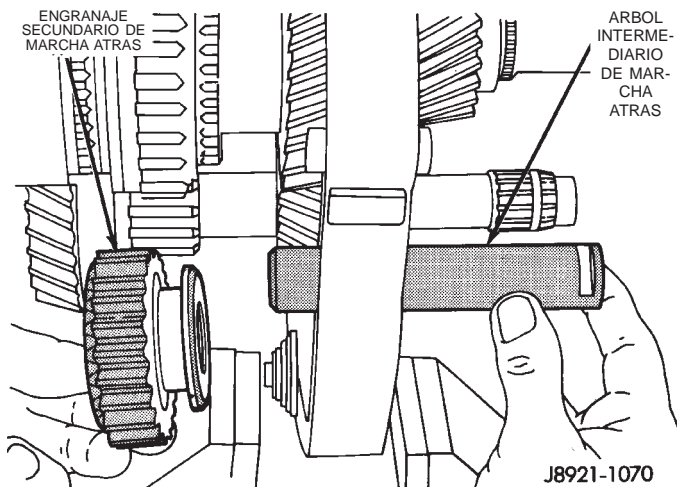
Desmontaje del eje y del engranaje secundario de marcha atrás
